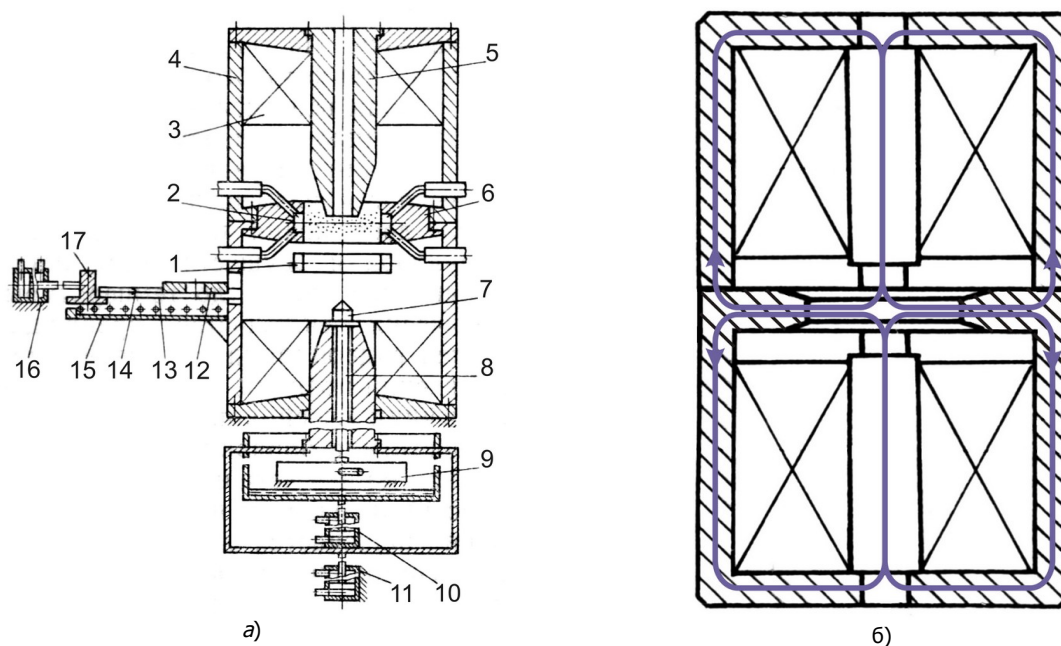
Установка для ТОМП тонкостенных деталей кольцевой формы при индукционном нагреве (а) и схема магнитного потока, проходящего через деталь (б)
